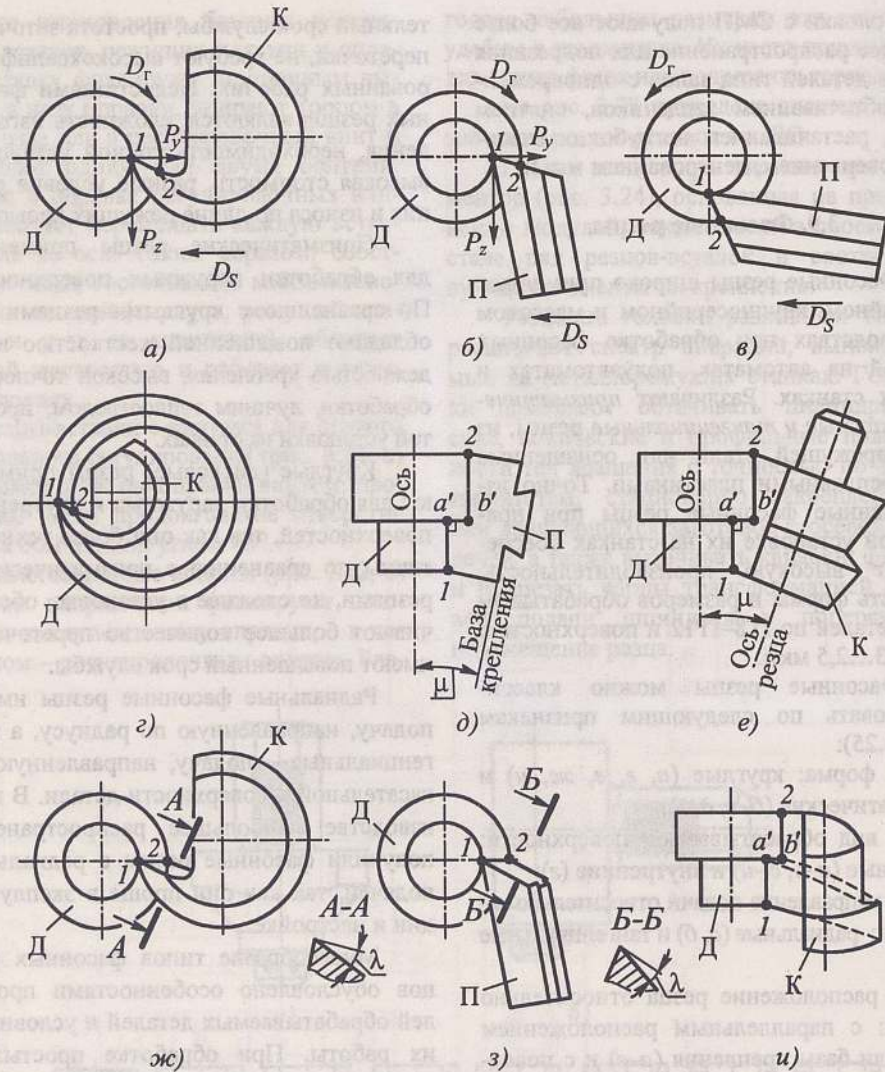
Типы фасонных резцов: Д – деталь; К – круглые резцы; П – призматические резцы; 1–2 – режущие кромки;  $D_r$  – главное движение;  $D_s$  – движение подачи
